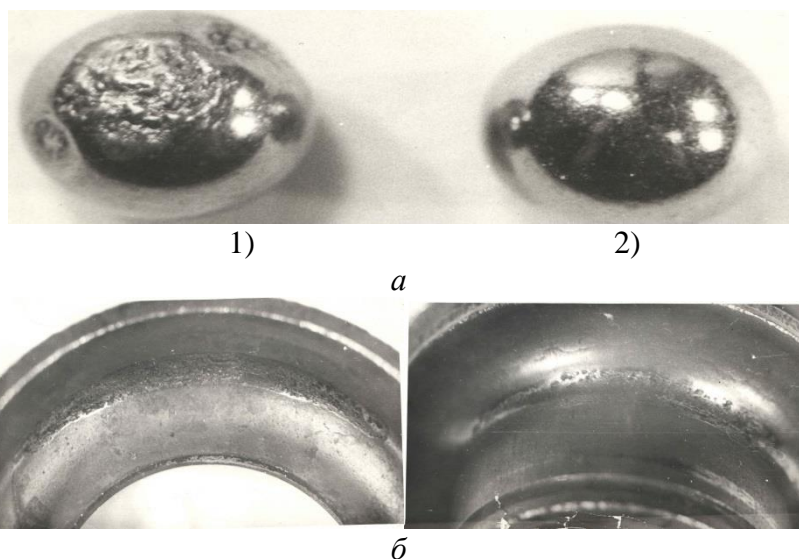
1) чистая смазка, 2) содержащая сверхпластичный сплав
